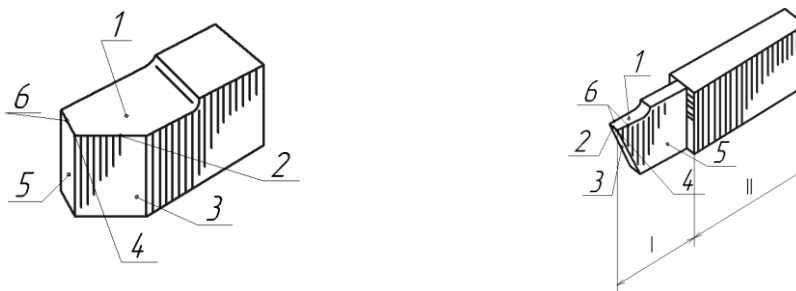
Элементы рабочей части токарного проходного резца: 1 – передняя поверхность; 2 – главная режущая кромка; 3 – главная задняя
